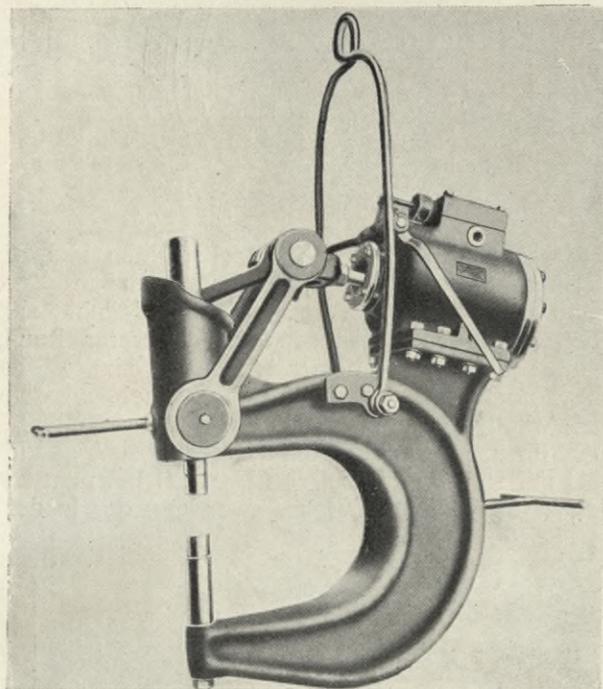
Pneumatische Kniehebelnietmaschine (Druckwerk)
